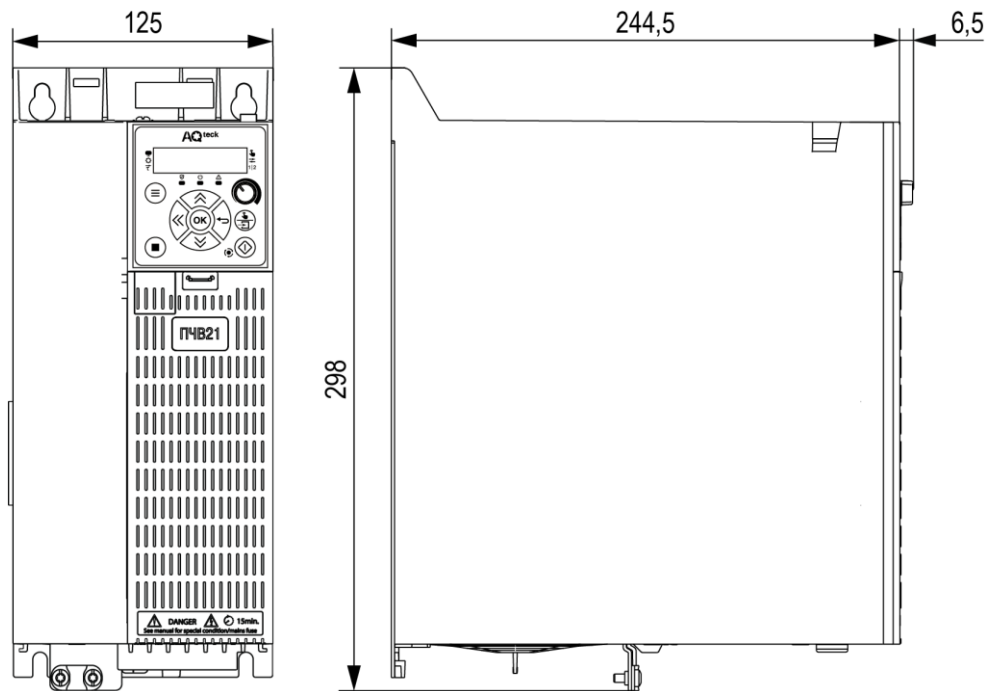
Габаритні розміри ПЧВ у корпусі 6
